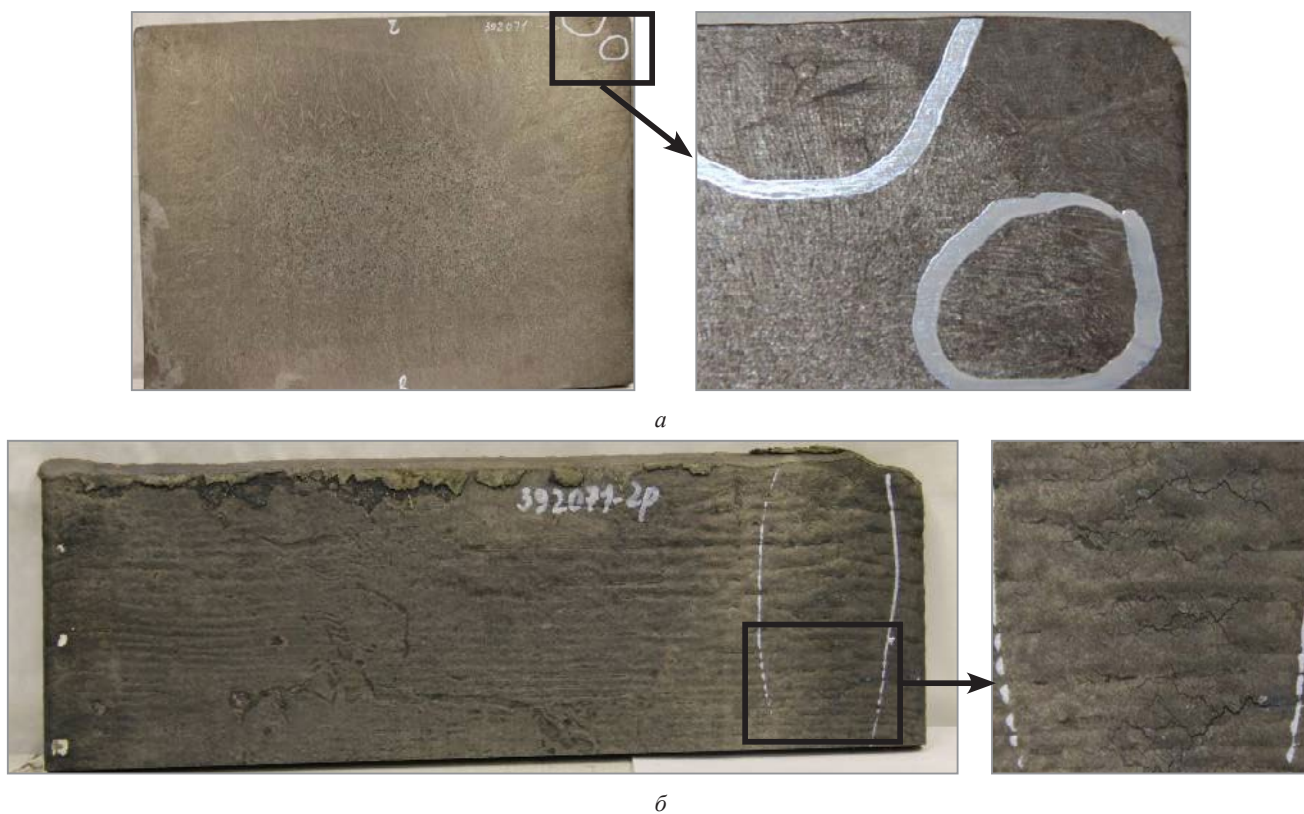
Непрерывнолитая заготовка сечением 300x400 мм стали марки 18Г2АФ:
